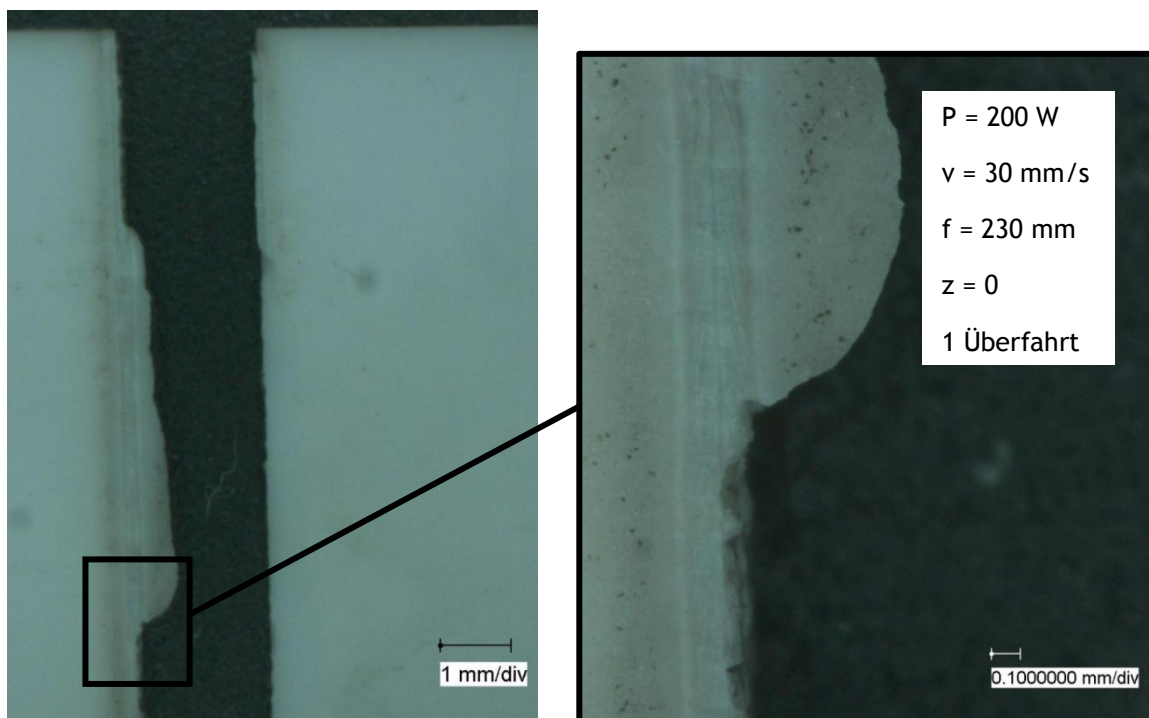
Draufsicht auf manuell gebrochene Stumpfstoßschweißung
